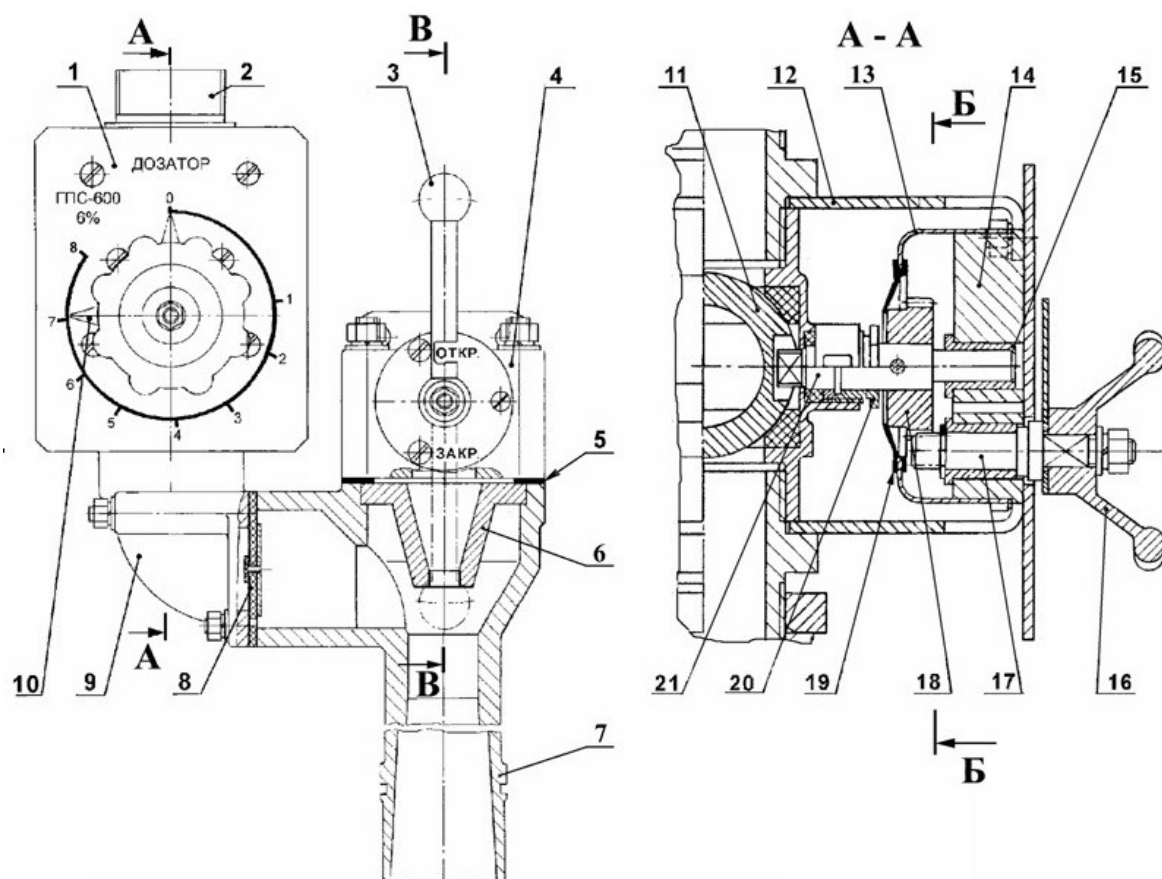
Пеносмеситель насоса НЦПН-40/100: 1 – дозатор; 2 – патрубок подвода пенообразователя; 3 – рукоятка включения эжектора; 4 – корпус крана эжектора; 5 – прокладка; 6 – сопло; 7 – диффузор; 8 – обратный лепестковый клапан; 9 – соединительный патрубок; 10 – стрелка; 11 – шар крана; 12 – кронштейн; 13 – кожух; 14 – корпус; 15 – втулка; 16 – маховик; 17 – вал-шестерня; втулка; 18 – колесо цилиндрическое прямозубое; 19 – манжета; 20 – гайка; 21 – валик.
